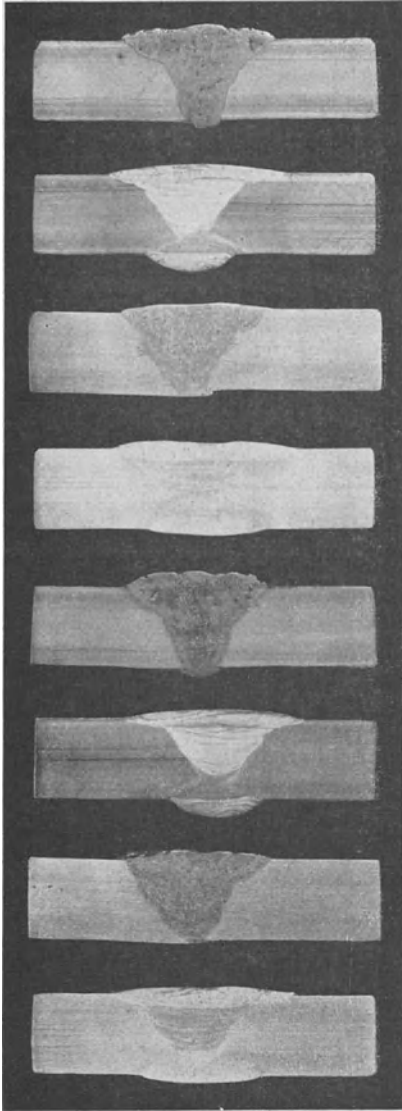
Grobgefügebilder von Schweißnähten.
